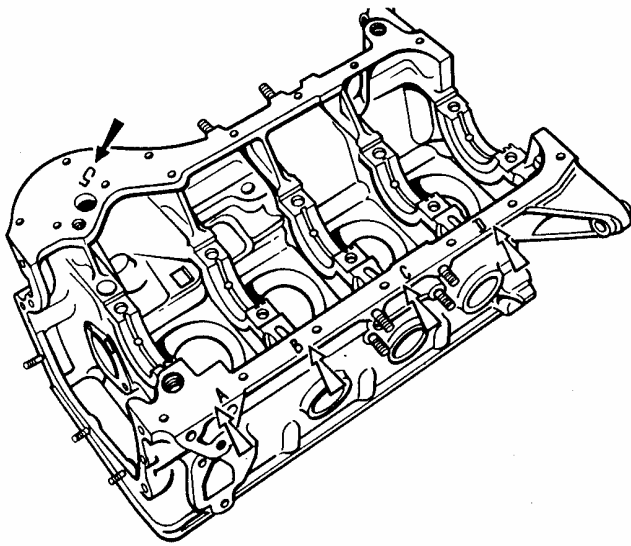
Marcación del grupo dimensional de los cilindros en el bloque (flechas blancas) y del número convencional del bloque de cilindros (flecha negra)
